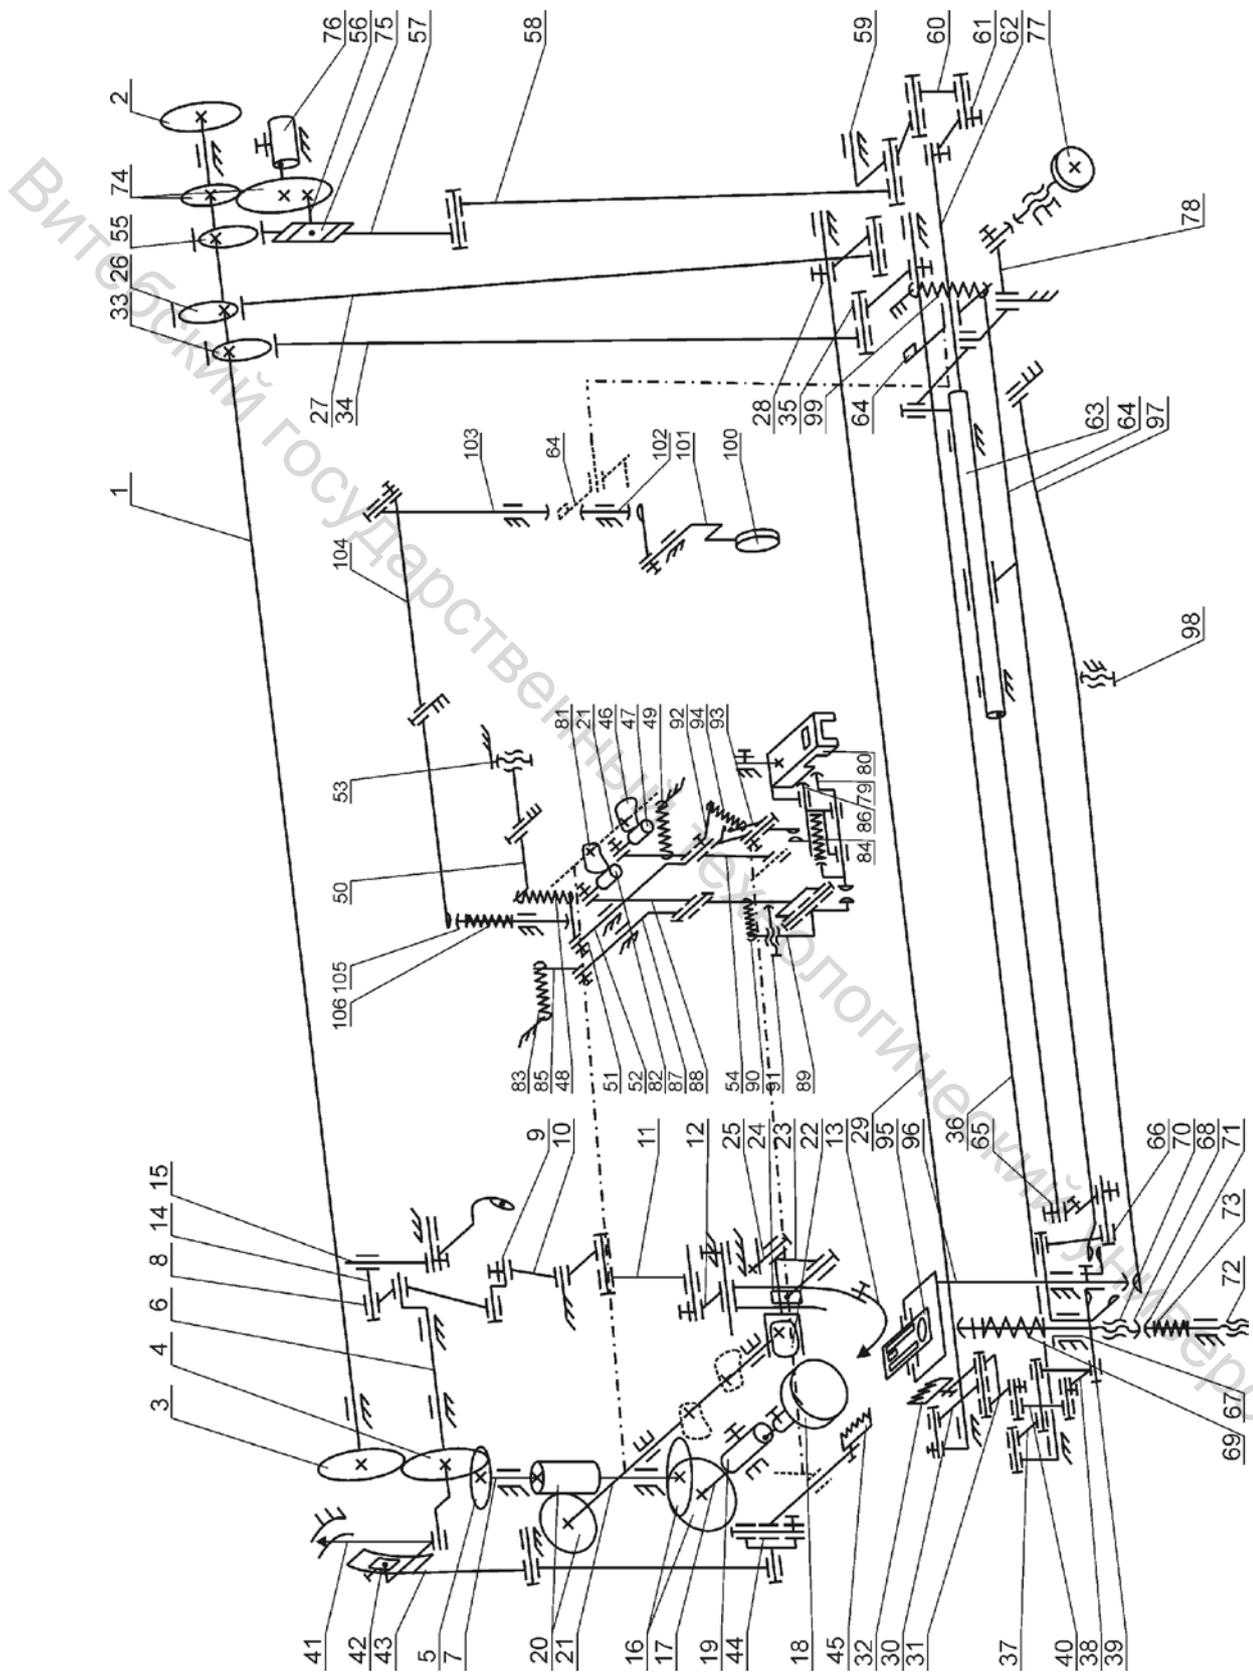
Кинематическая схема машины 30-210 Union Special
